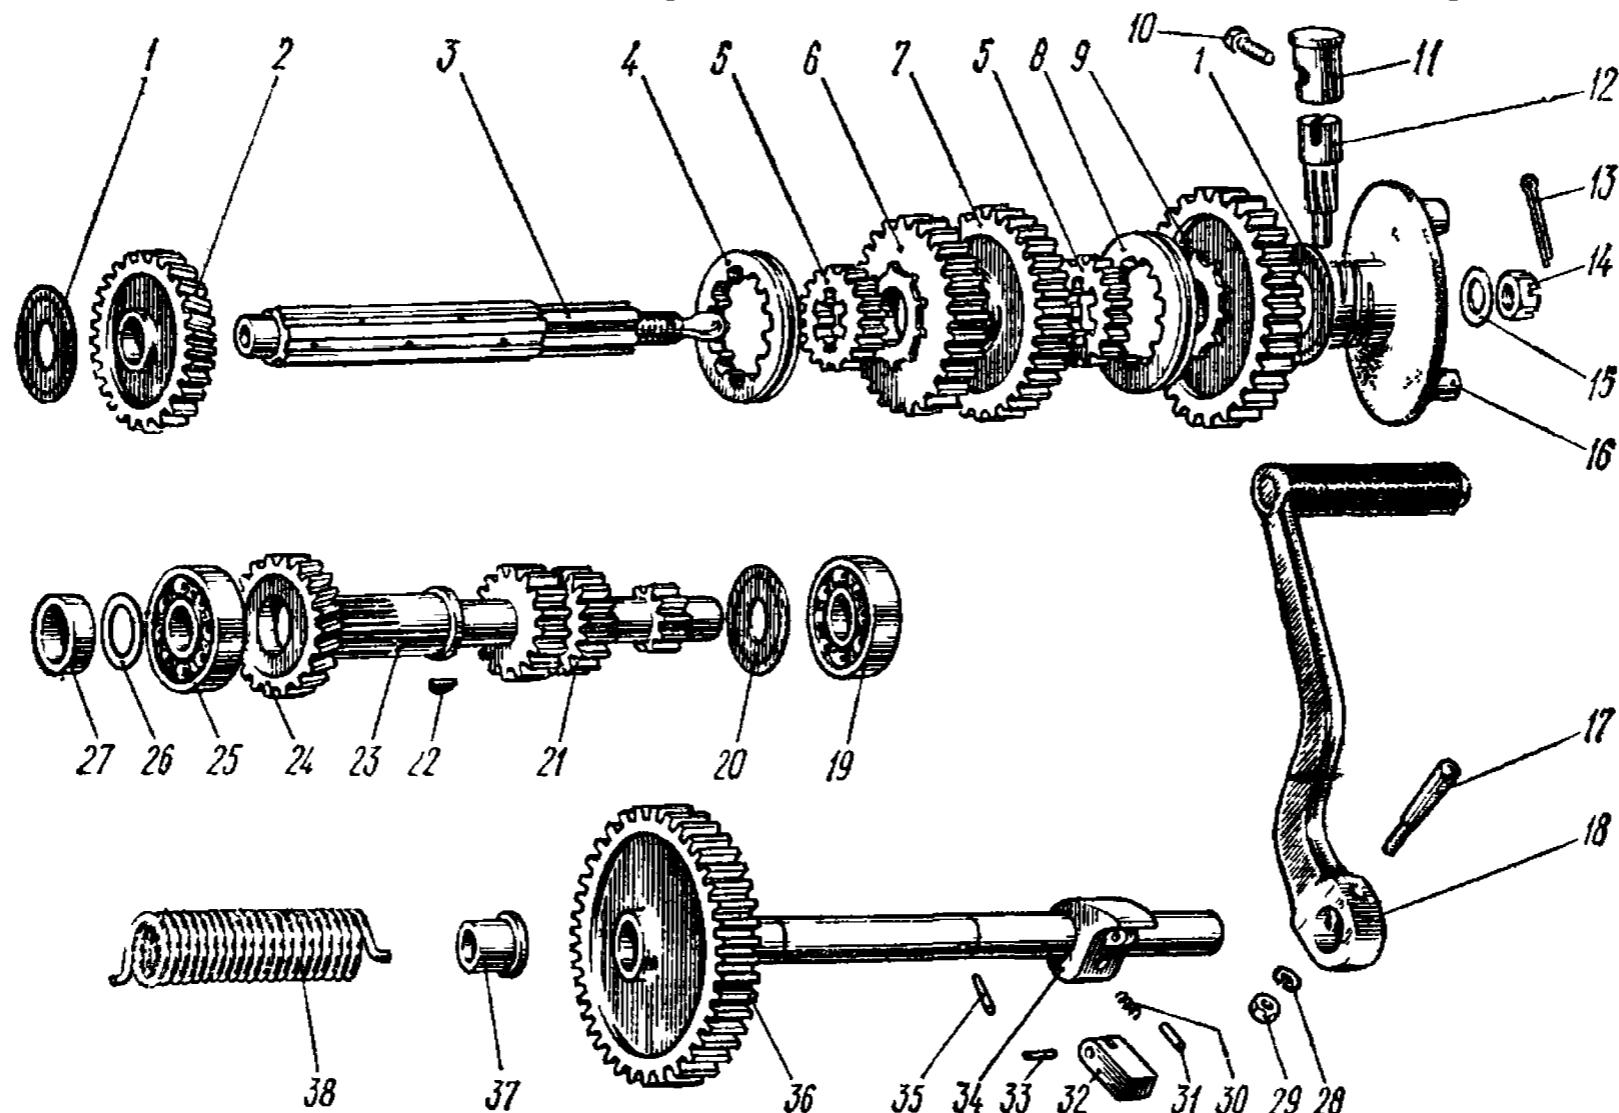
Валы и зубчатые колеса коробки передач мотоциклов «Урал»
